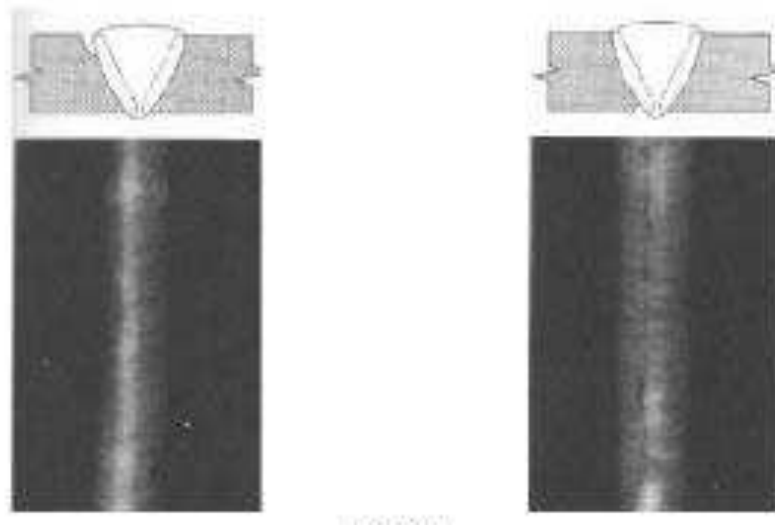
Socavaduras o mordeduras de borde en soldadura.
